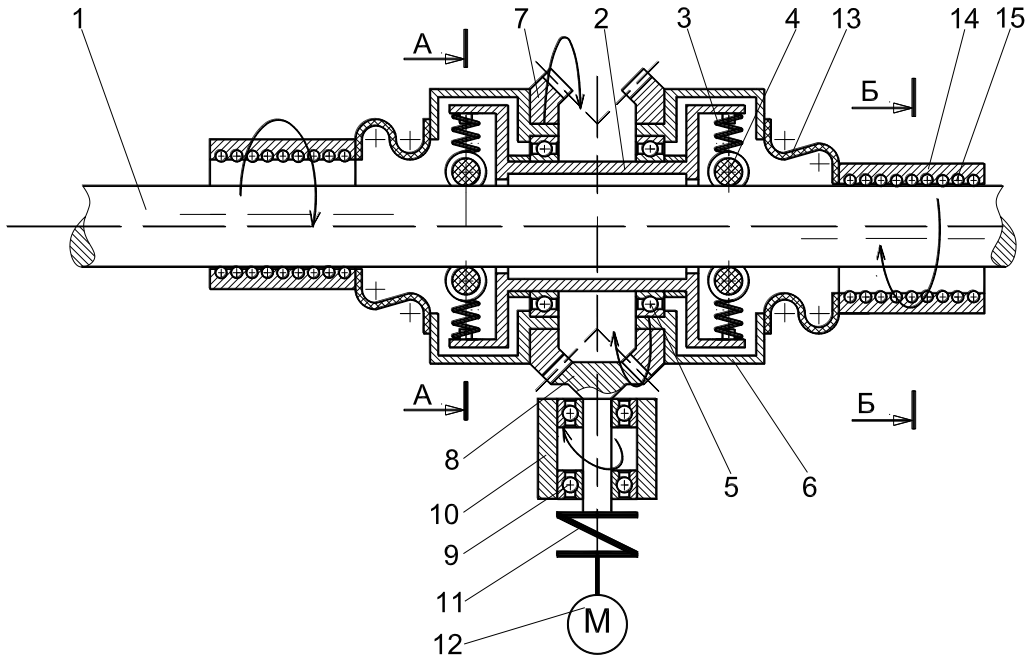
Принципова схема зміцнювача для поверхневого пластичного деформування торсіонних валів та зовнішніх поверхонь циліндричних довгомірних деталей
